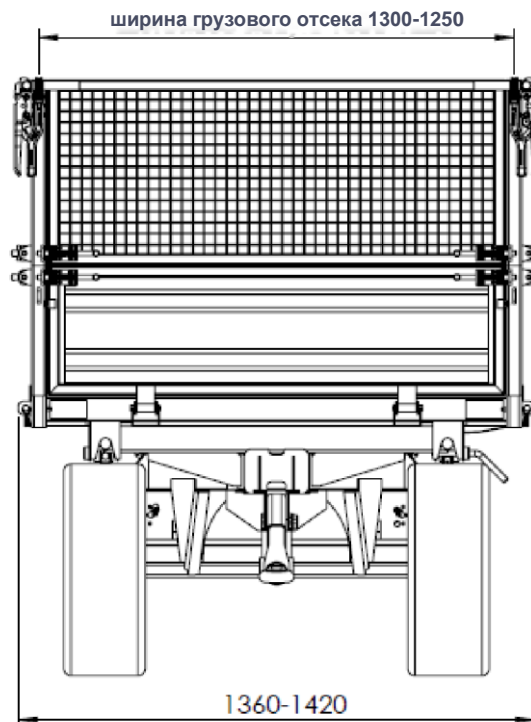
Размеры прицепа Т932/2 - вид спереди
